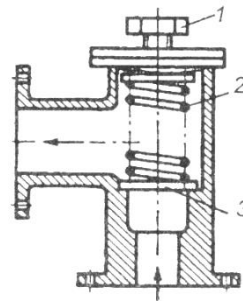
Пружинный клапан: 1 – регулировочный винт; 2 – пружина; 3 – клапан
